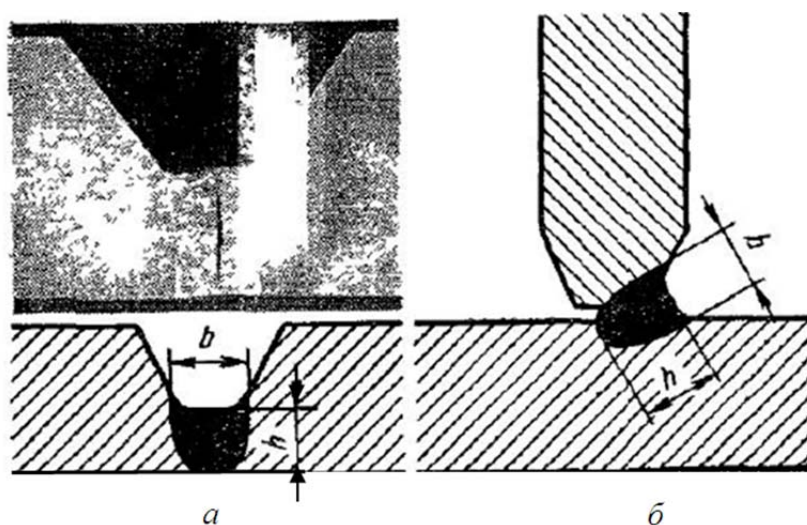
Перший шар багат шарового шва: *а* — стыкового; *б* — кутового, з обробленням кромок
